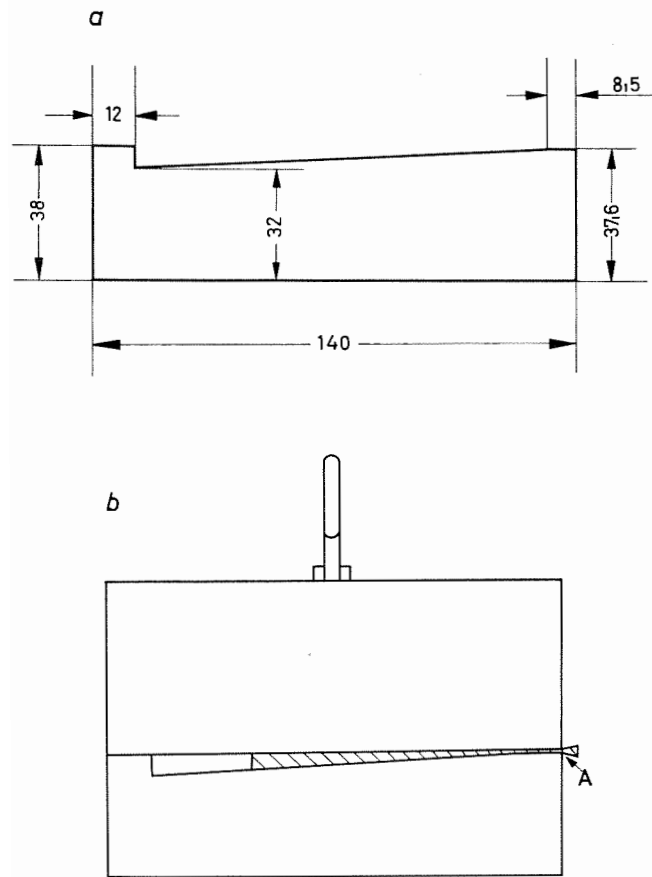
a: Querschnittszeichnung des Amboßes; b: Querschnittsskizze mit eingelegtem Prüfling (ca. 100 mm) nach dem Schlag.
